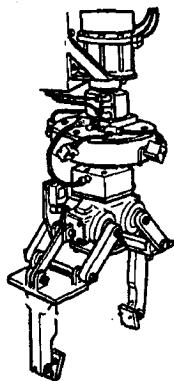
Повноповоротний захватний пристрій з вібродвигунами
